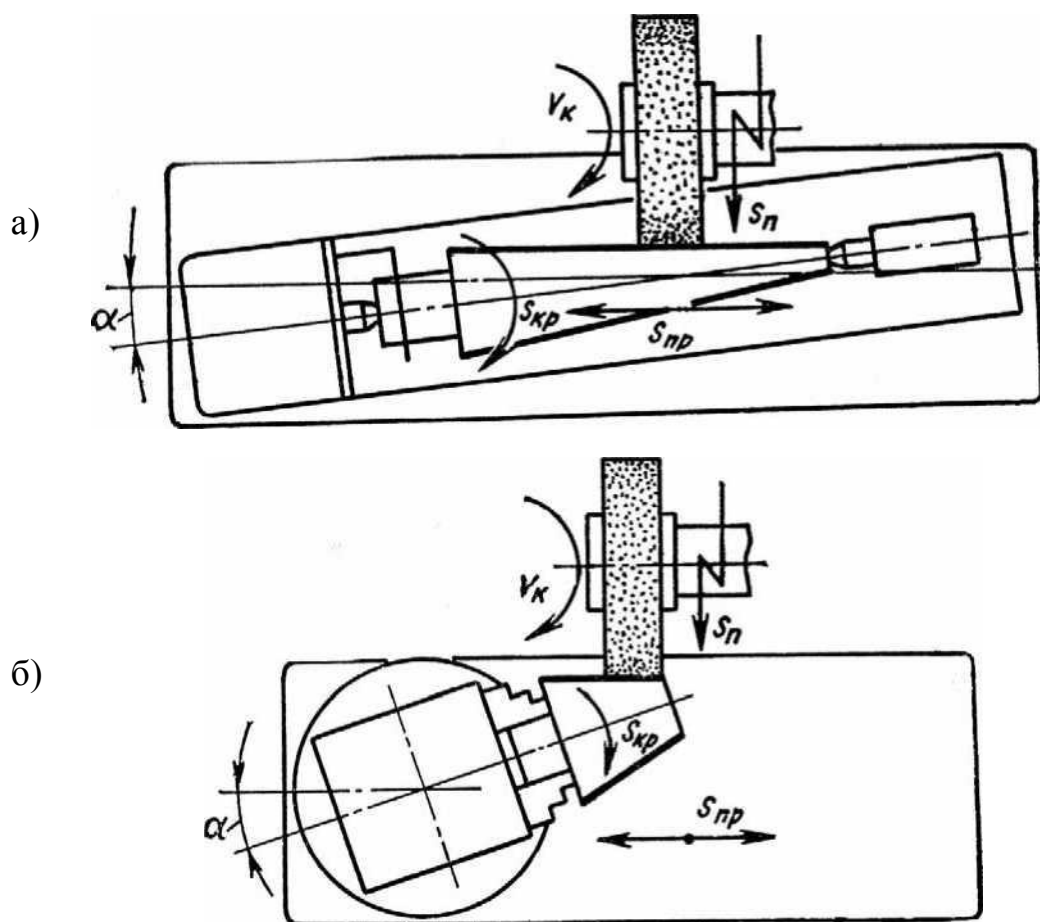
Схемы шлифования конических поверхностей: а - закрепление заготовки центрах; б - консольное закрепление заготовки
